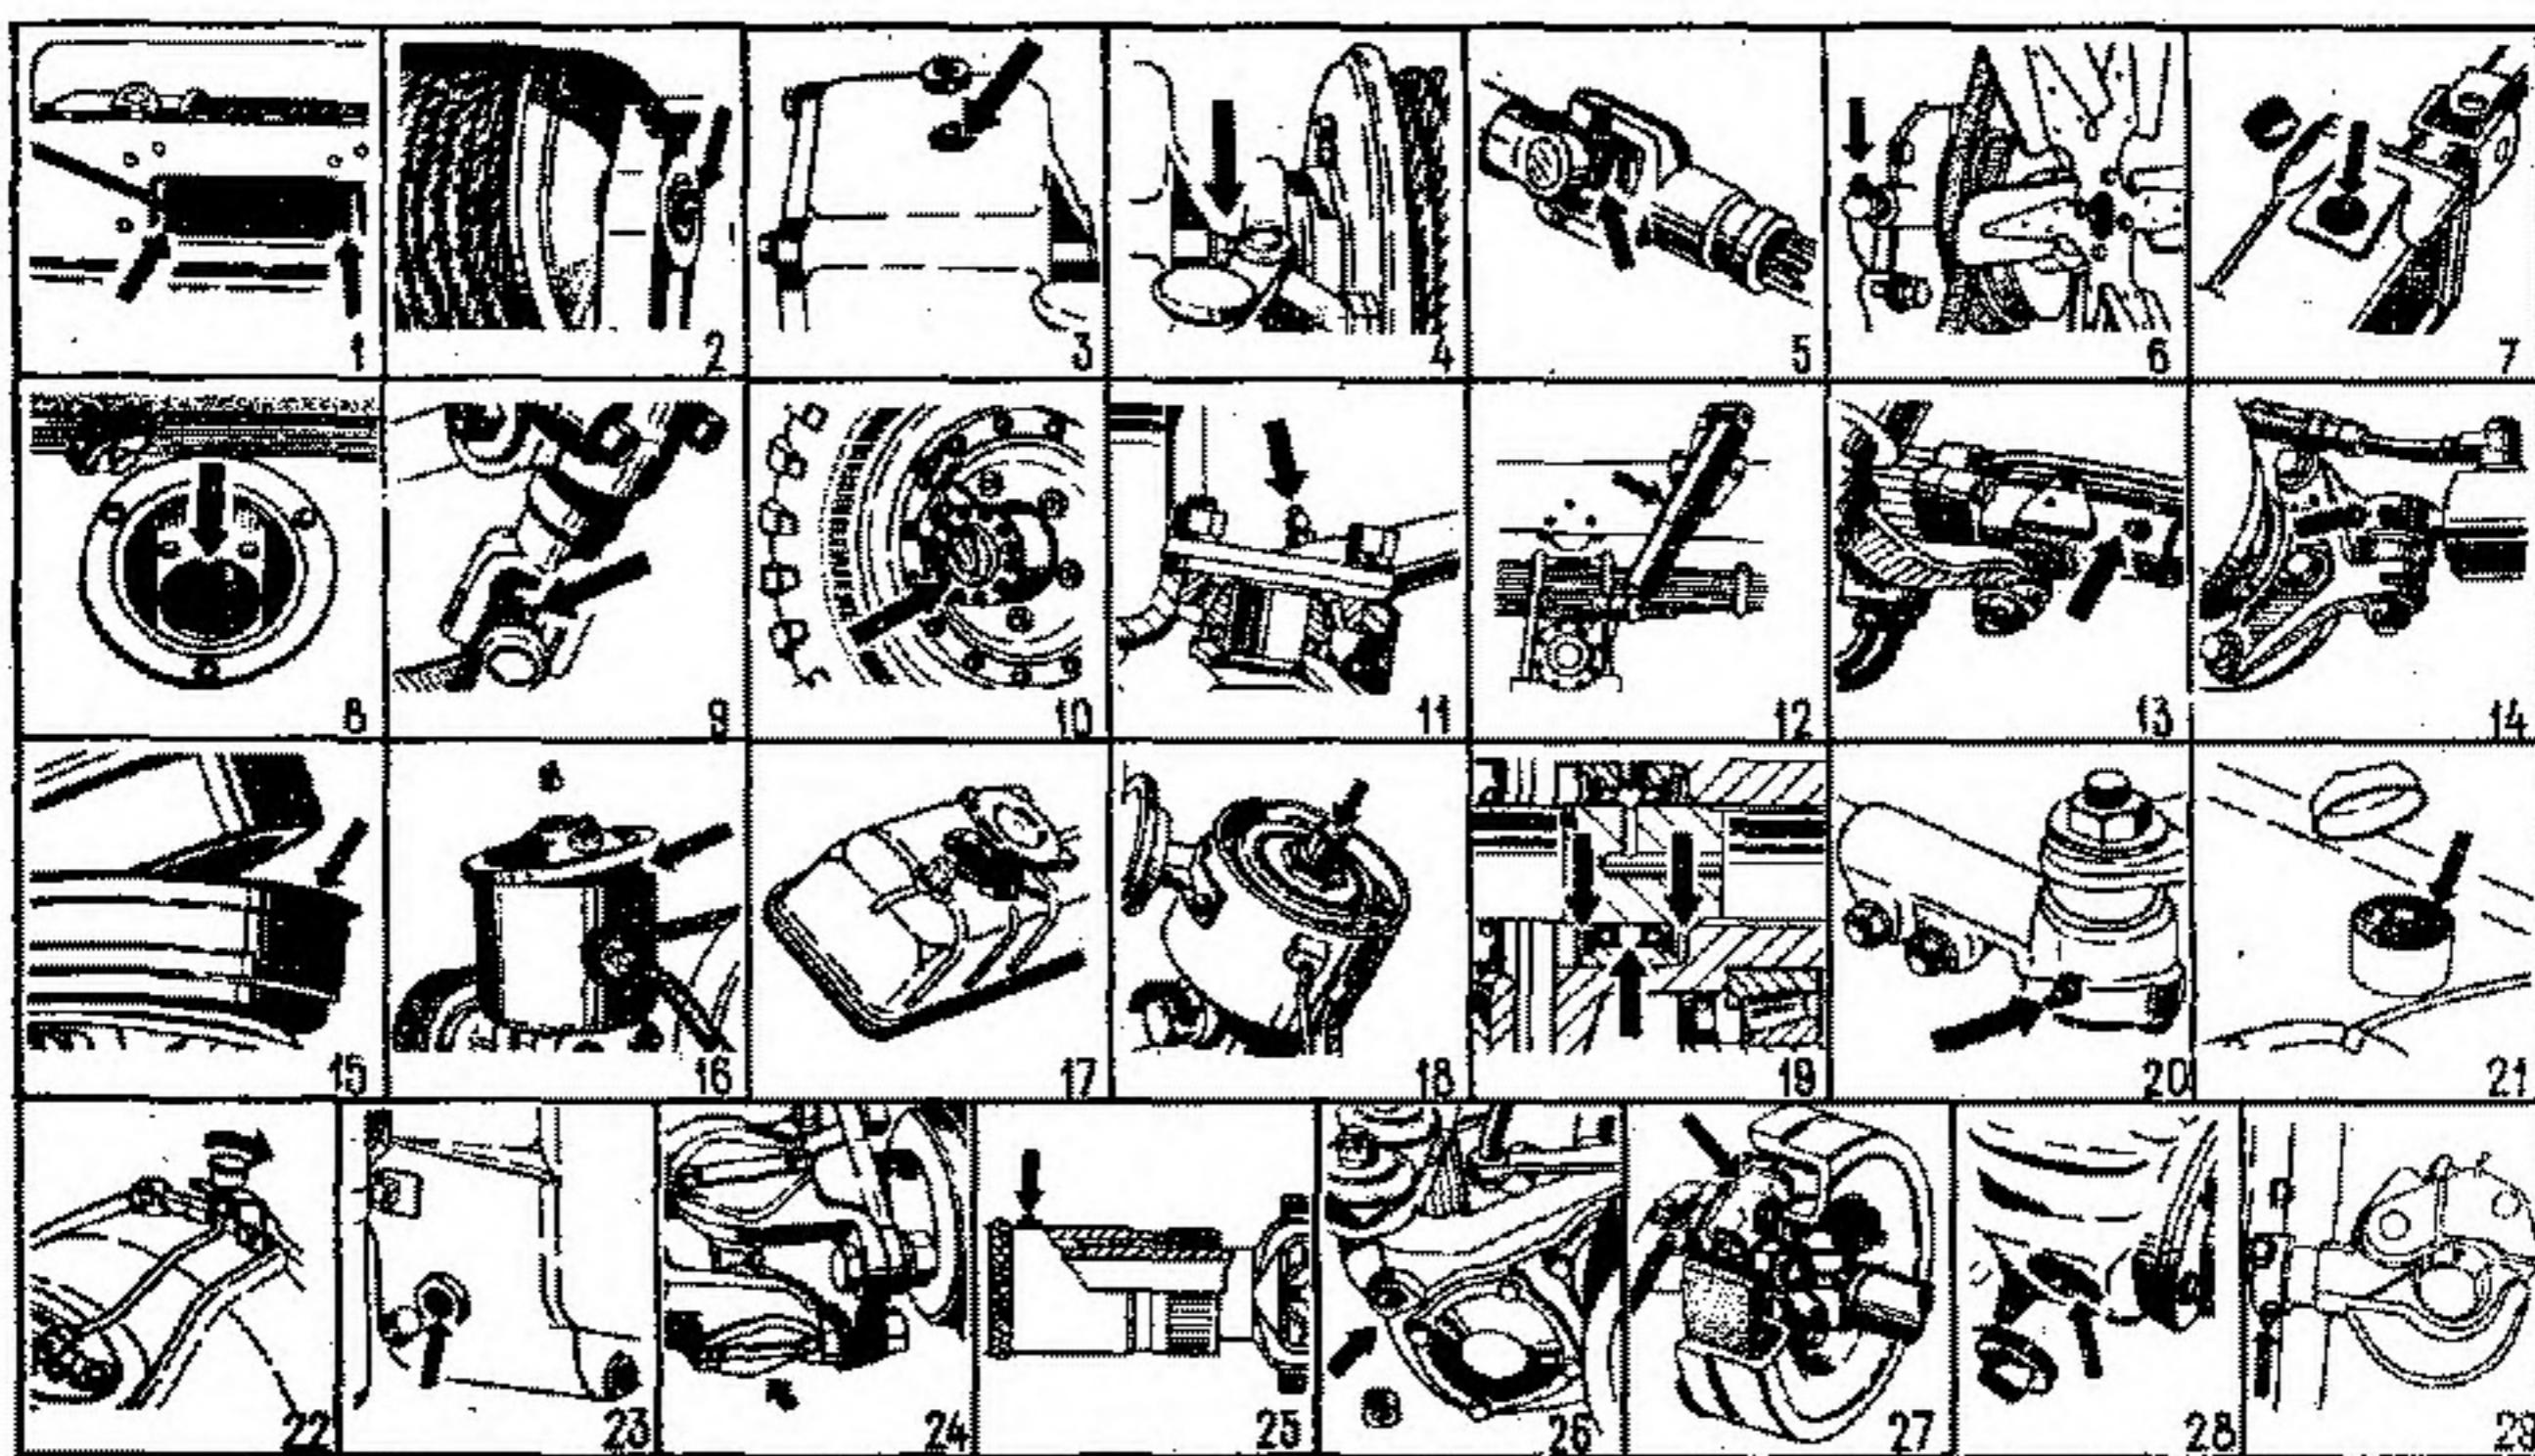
Схема смазки автомобиля ГАЗ-66-11
